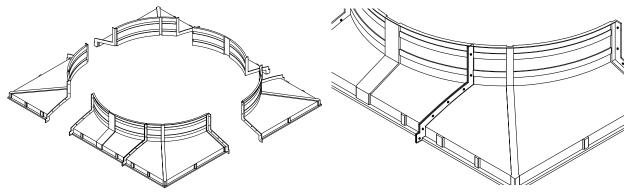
Ensamble de la sección de la campana de una torre modular RTMTC.
